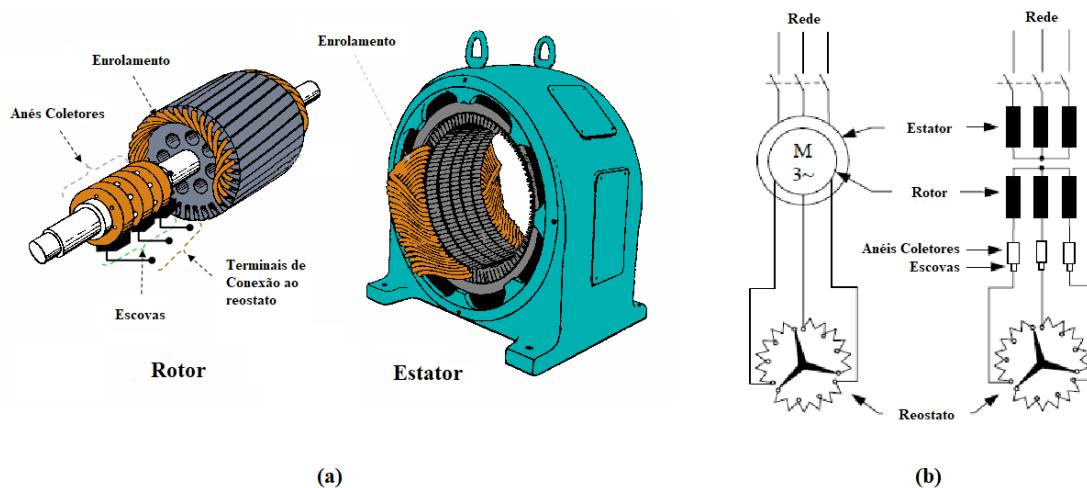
Vista explodida de um motor de rotor bobinado. (b) Diagrama de ligação de um motor de rotor bobinado a um reostato. Fonte: Extraído de [31].
